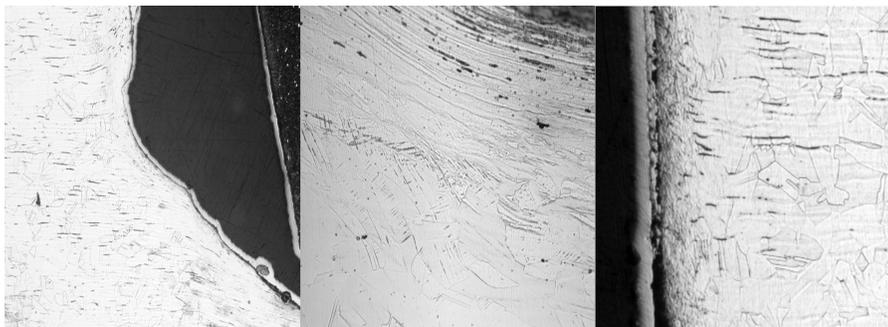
Корень стружки – для двух режущих кромок спирального сверла - часть материала прижимается поперечной режущей кромкой
